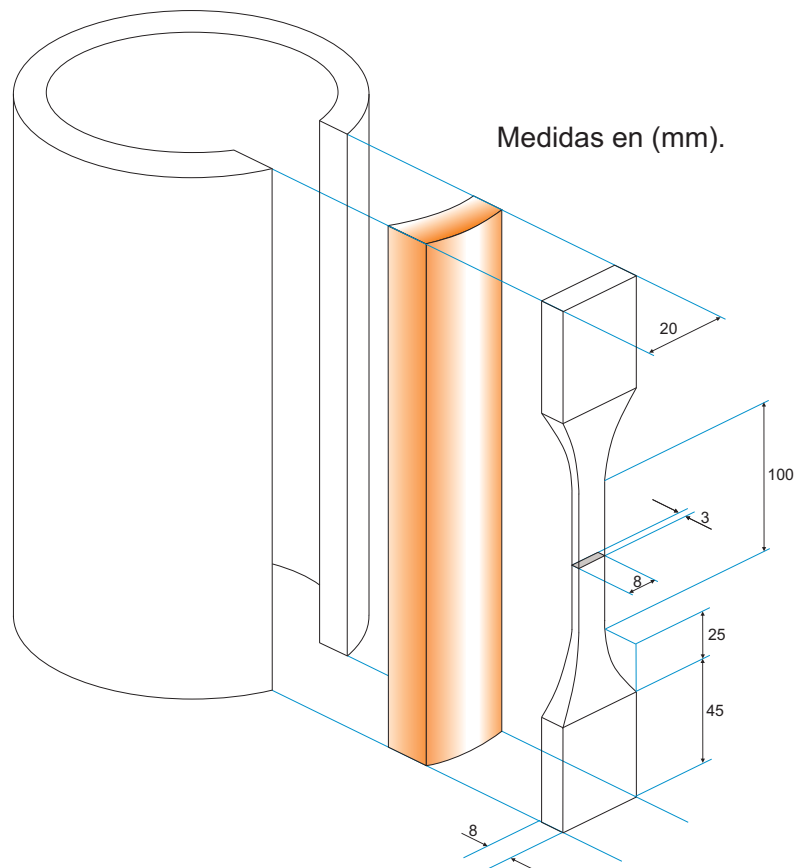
Esquema de extracción y geometría de las probetas para los ensayos de tracción. Fuente: Autor.
